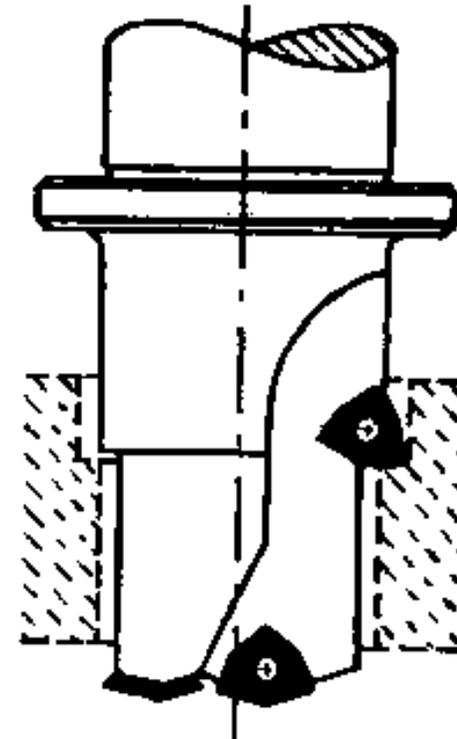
Punta a forare a "lancia" con inserto a fissaggio meccanico.
